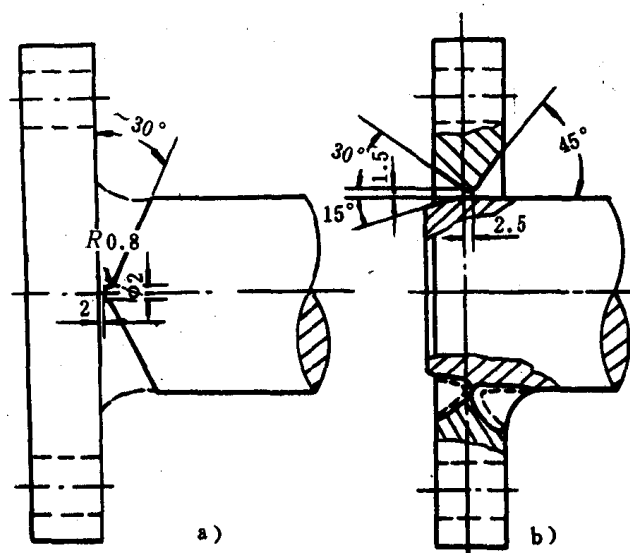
18 焊接凸缘联轴节焊接结构尺寸图
